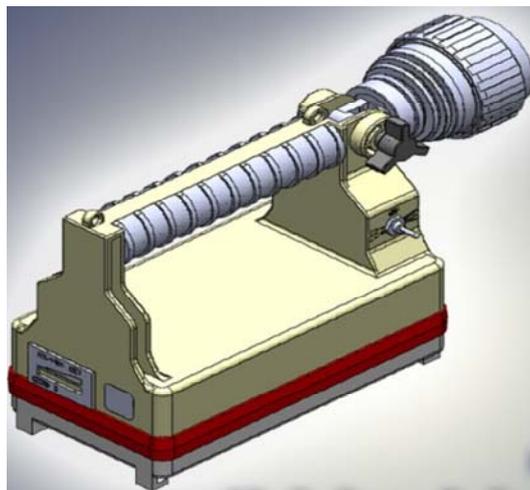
Внешний вид фонаря «АЗС-1-001 СВЕТ»
